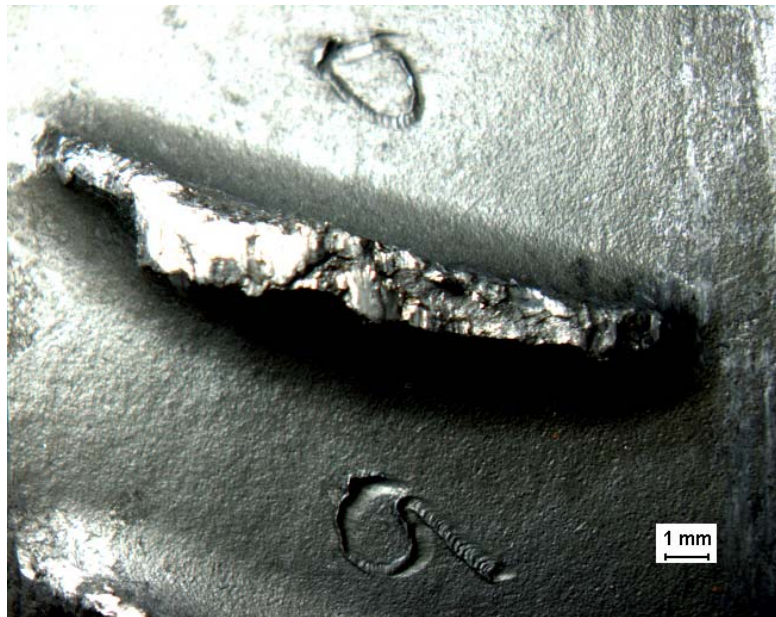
Roten till det kompressorblad i tredje steget där utmattningsbrott kunde iakttagas.
